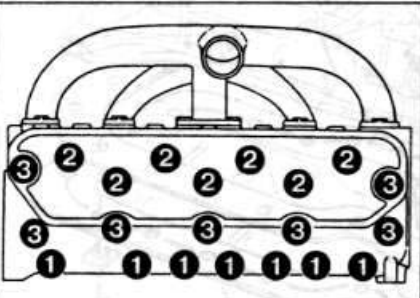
Расположение болтов крепления головки цилиндров:
